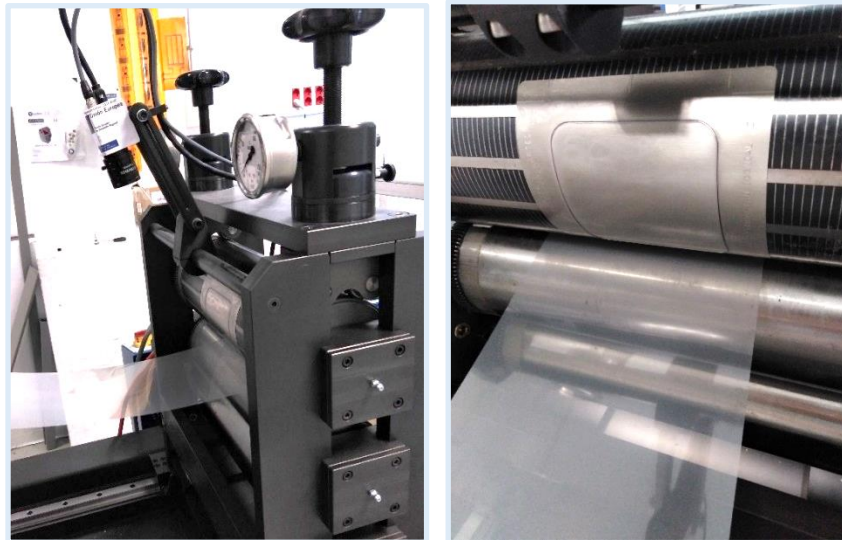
Equipo para troquelado integrado en línea R2R y detalle de útil diseñado y fabricado para el corte de probetas rectangulares
